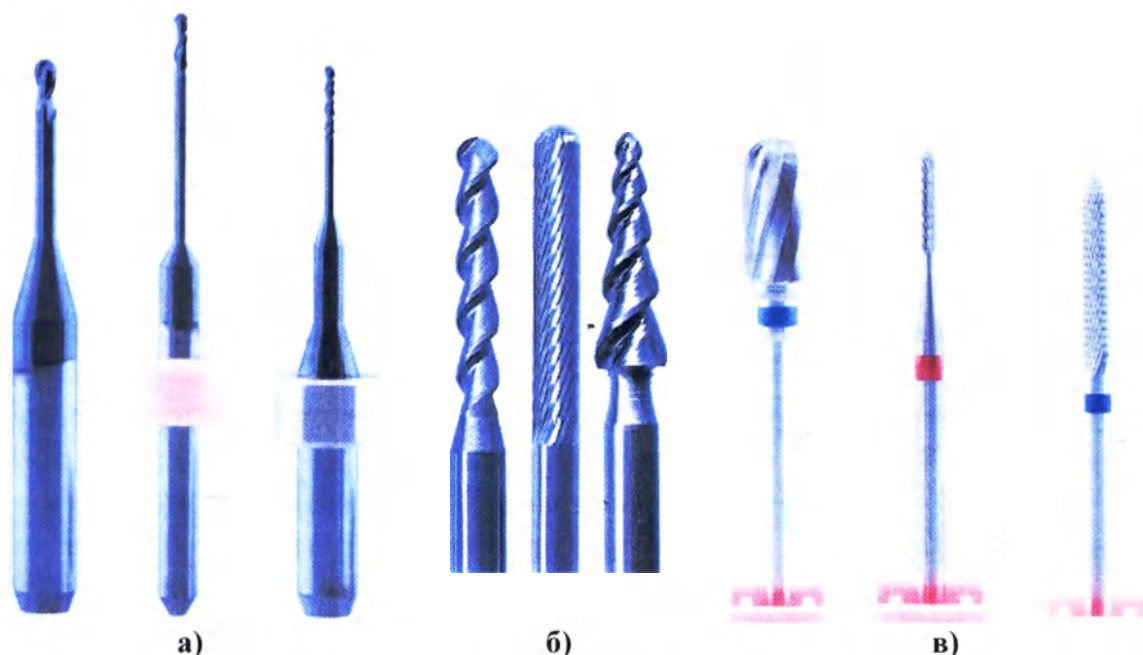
Внешний вид некоторых артикулов медицинского изделия в вариантах исполнения CAD/CAM burs (а), Milling Technique (б), Tungsten Carbide Burs (в).
